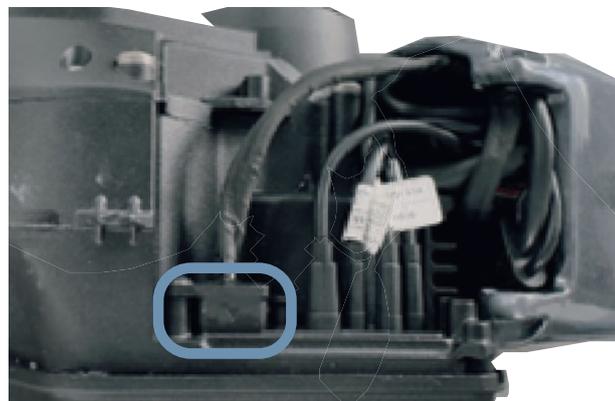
Markierten Stecker mit Schraubendreher lösen
